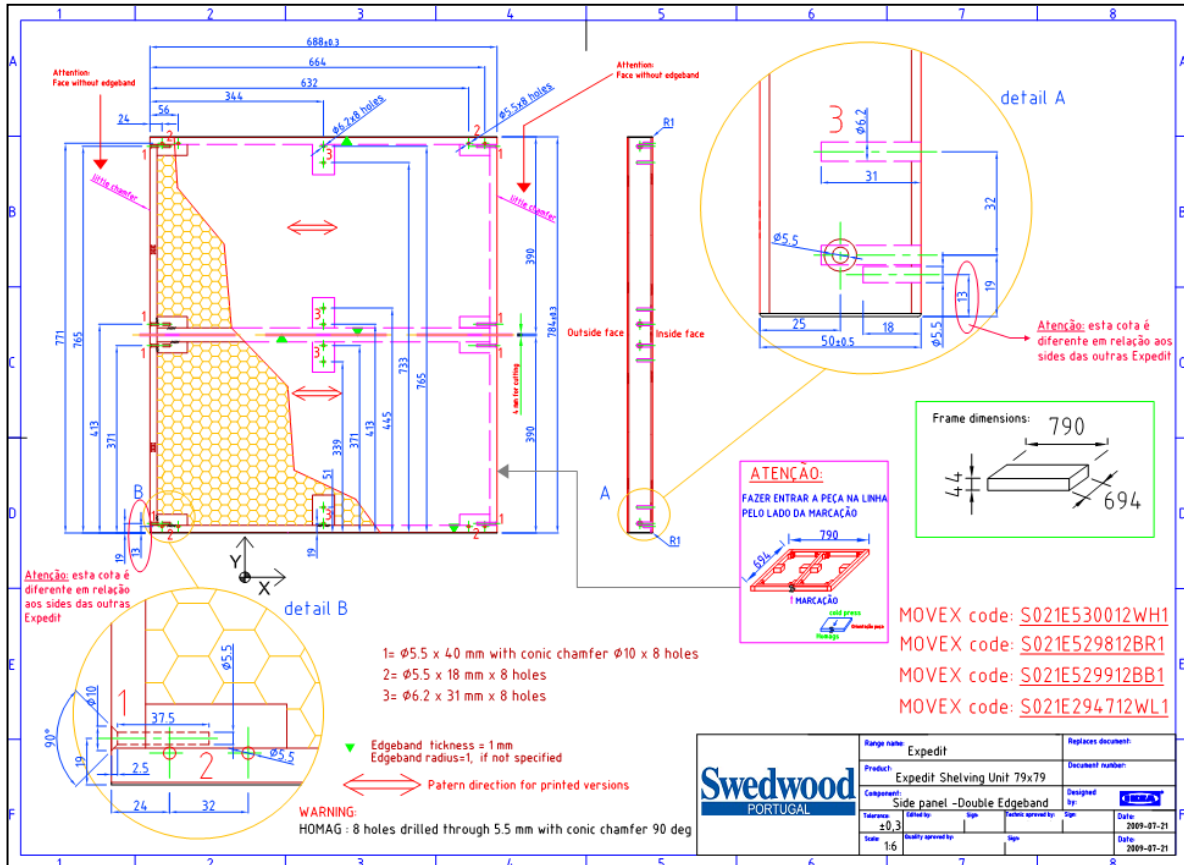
Desenho técnico utilizado para controlo da furação.
